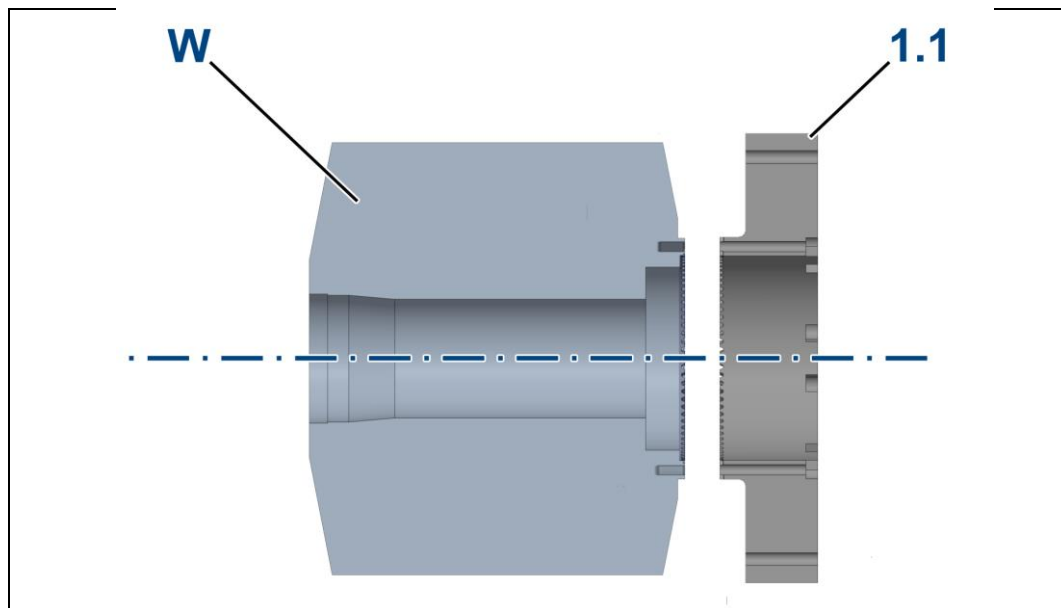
Getriebestern und Getriebe ausrichten (Beispiel) – W Hohlwelle des Getriebes (Modell) und 1.1. Getriebestern geschnitten
